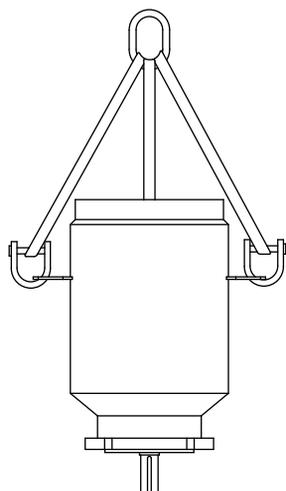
Пример правильного подъема двигателя с использованием подъемных проушин
